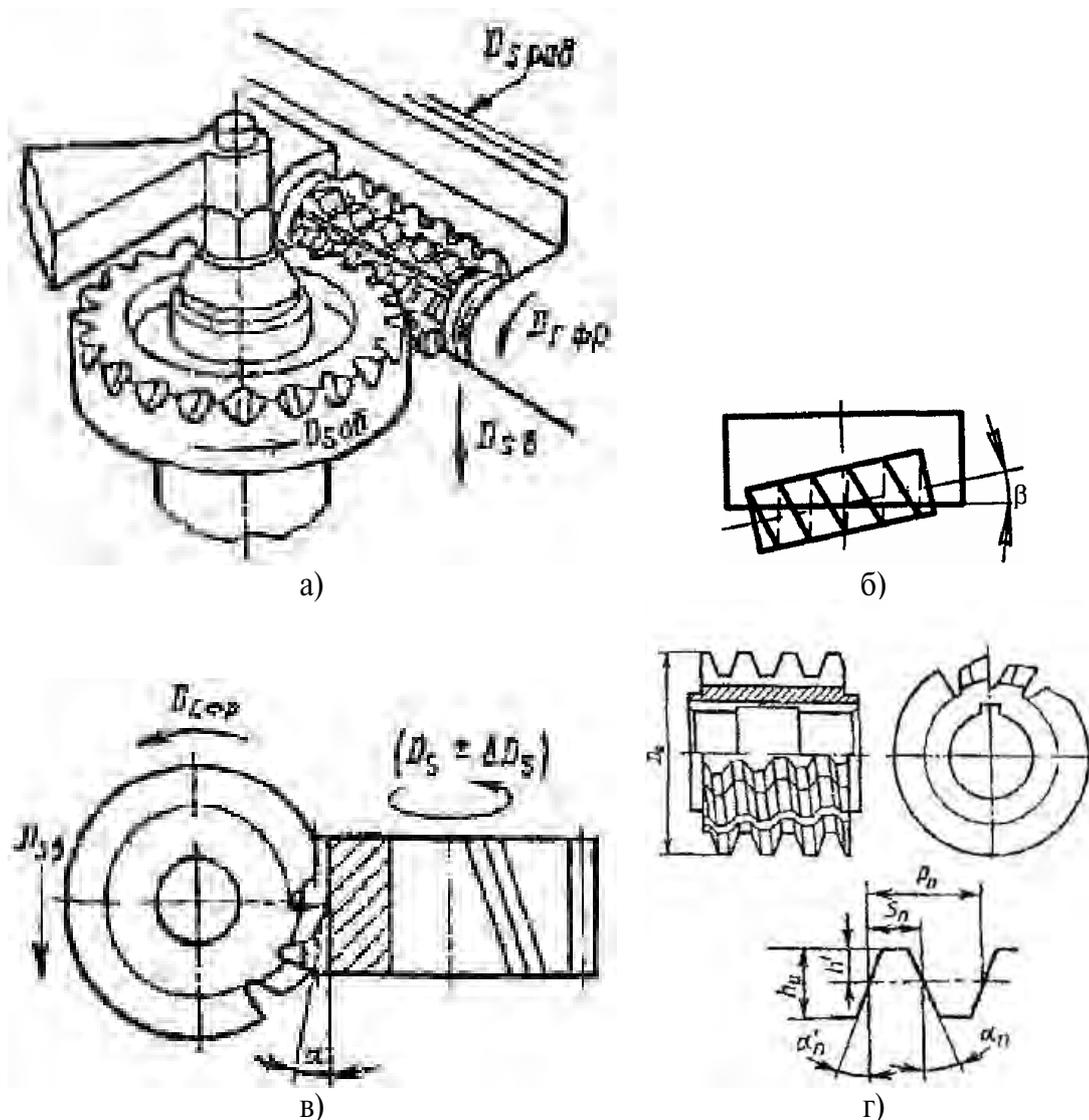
Схемы работы и конструкции червячных фрез
